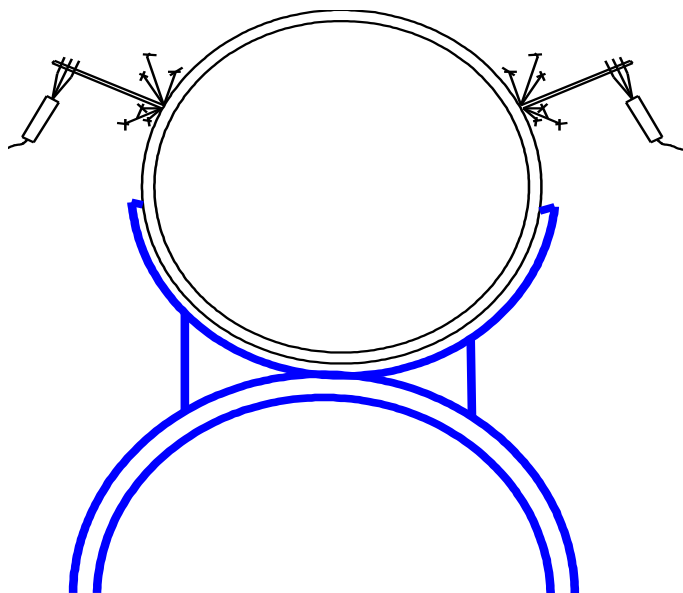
Сварка заполняющего и облицовочного слоя
